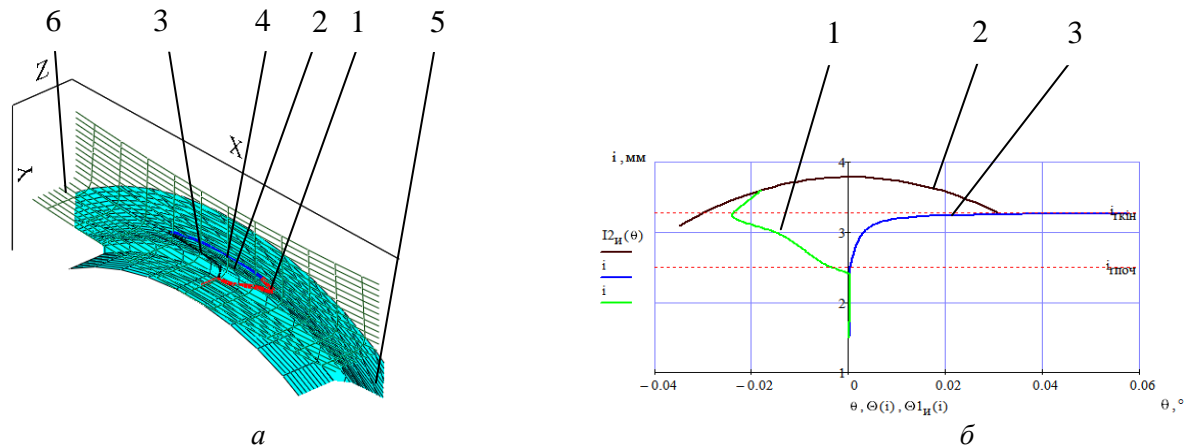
Перетин шліфувального круга і вала під час оброблення циліндричної поверхні: а – пляма контакту деталі зі шліфувальним кругом; б – лінії перетину шліфувального круга і вала
